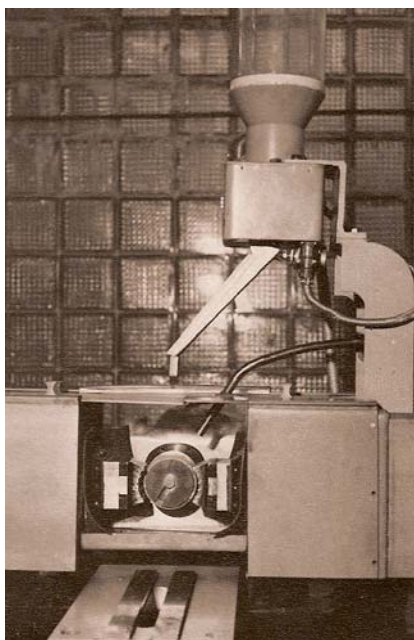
Фотография рабочей зоны станка СФТ 2.150.00.00.000
